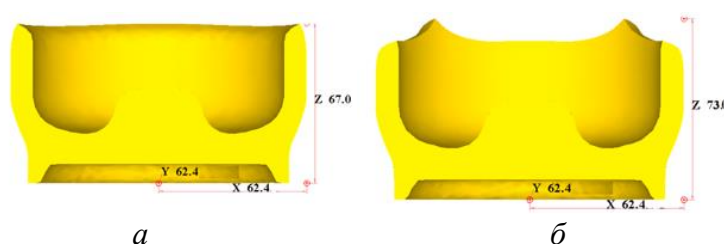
Форма і зовнішні розміри половин напівфабрикатів в розрізі після видавлювання: а - заготовки круглого перерізу, б - заготовки квадратного перерізу
